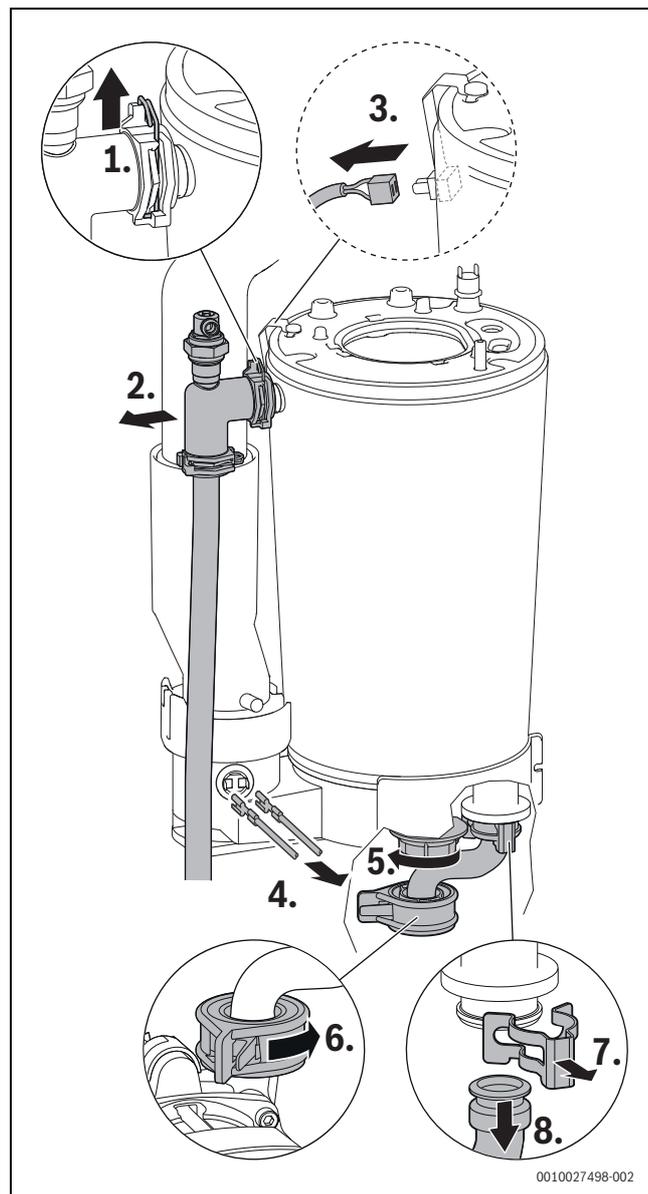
Détacher le tube de départ, retirer le câble et détacher le tube retour
